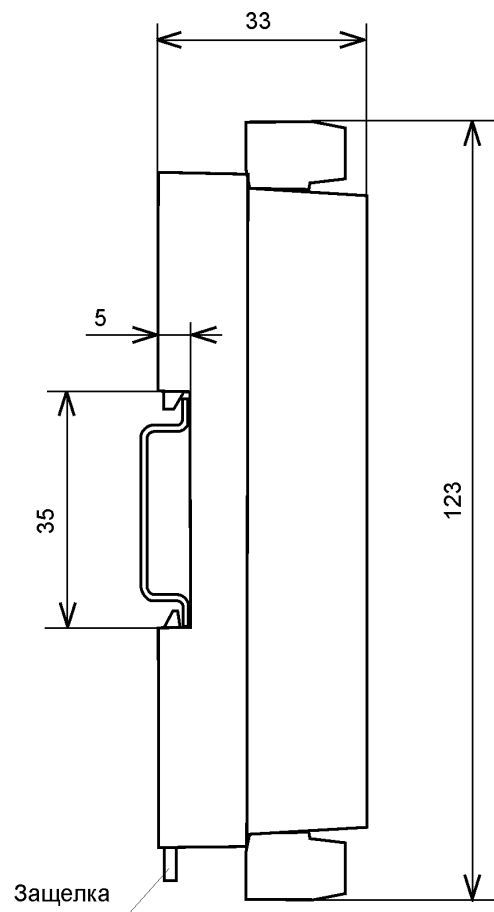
Габаритный чертеж модуля с креплением к DIN-рейке. Вид сбоку.
